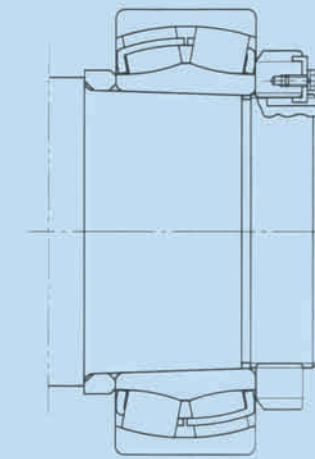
Конический вал, стопорный бугель (с дистанционным кольцом)
